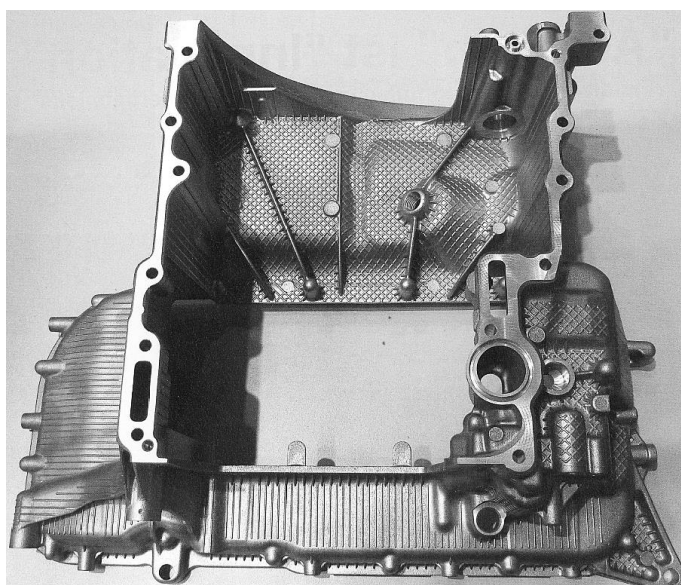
Gussteil aus einer Magnesiumlegierung mit zahlreichen Oberflächenstrukturen [136]
